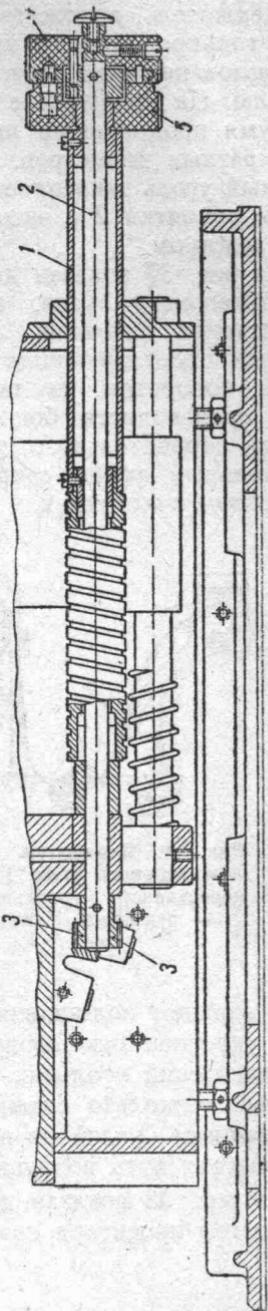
Шпиндельный механизм в разрезе: 1 — вал подачи держателя положительного угля; 2 — вал подачи держателя отрицательного угля; 3 — шестерня; 4 — передняя рукоятка; 5 — задняя рукоятка
